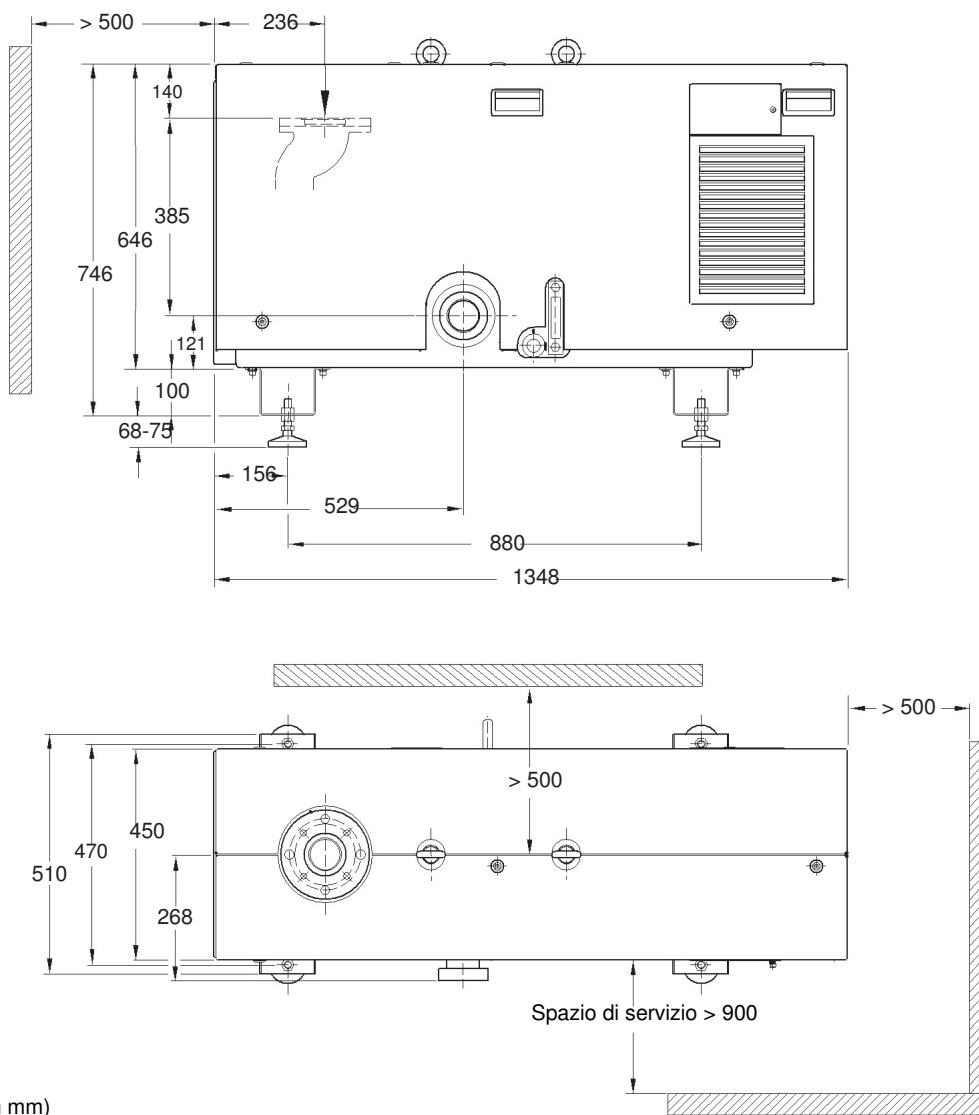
Disegno dimensionale della ScrewLine SP 250
